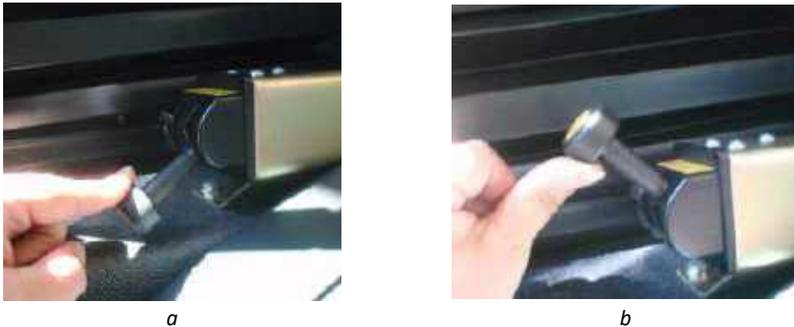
La vanne pneumatique commande le bord hydraulique: a) ouverture du bord, b) fermeture du bord
